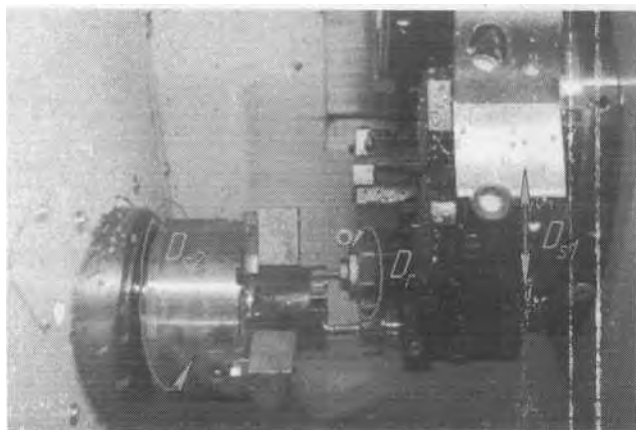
Обработка цилиндрической и плоской поверхностей детали на токарно-фрезерном станке с ЧПУ EMCOTum S45
